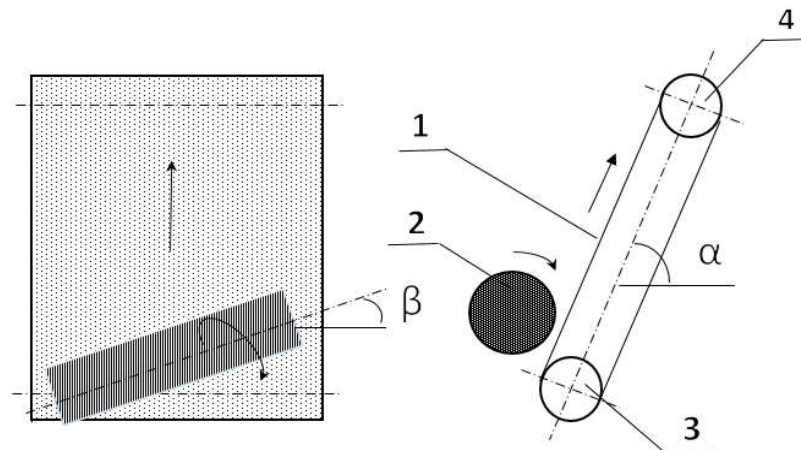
Схема вдосконаленого очищувального робочого органу: 1 – похила пальчаста гірка; 2 – валець з еластичною щіткою; 3 – нижній приводний барабан; 4 – верхній напрямний барабан
